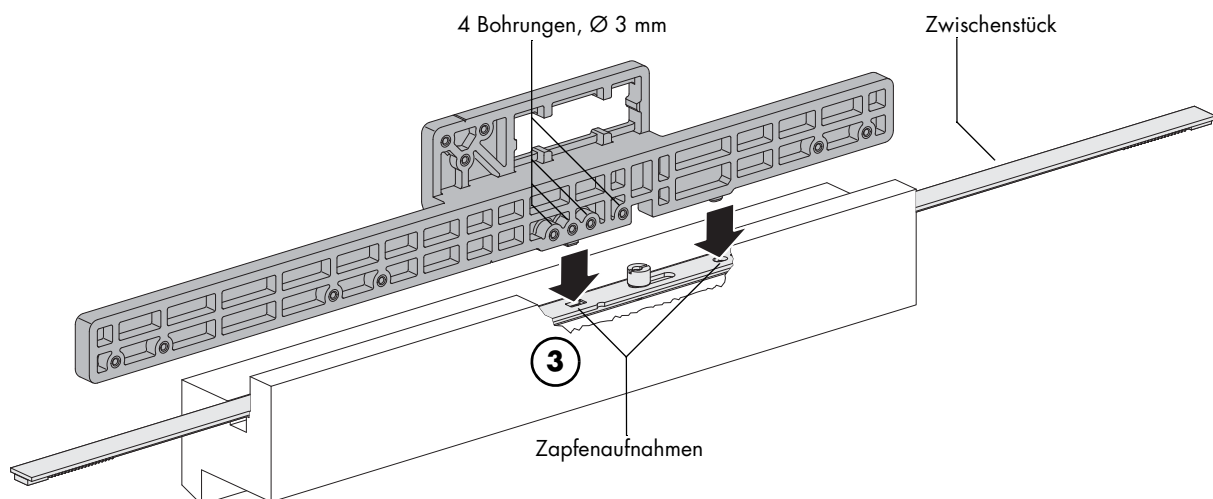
Bohrungen mit Bohrlehre am Holzprofil
